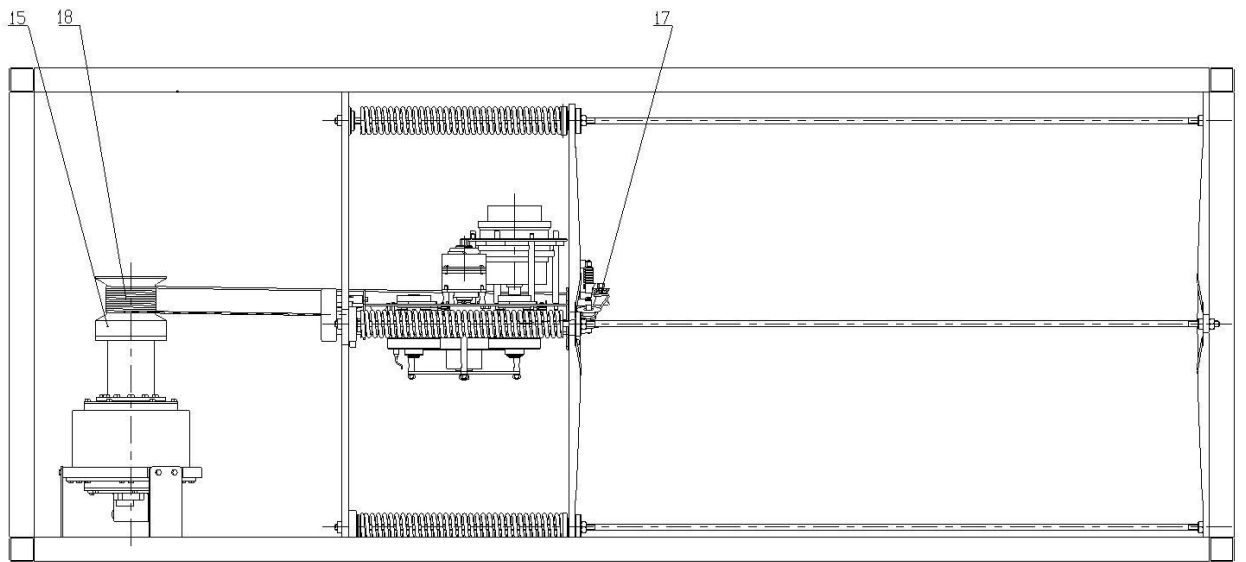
Общая компоновка лабораторного стенда (вид сверху)
